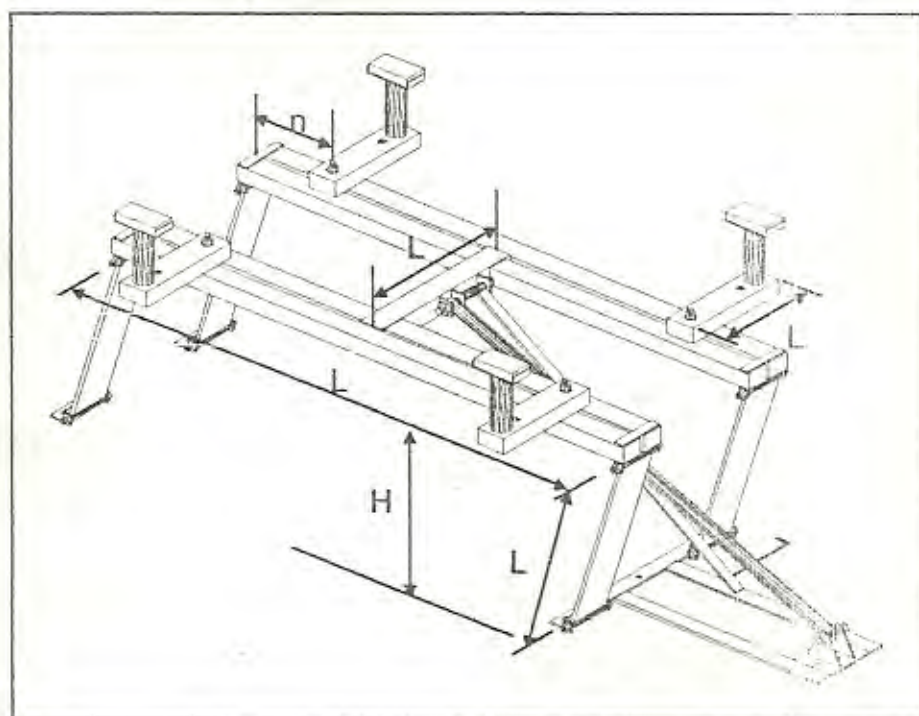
DIMENSIONES PRELIMINARES ELEVADOR
